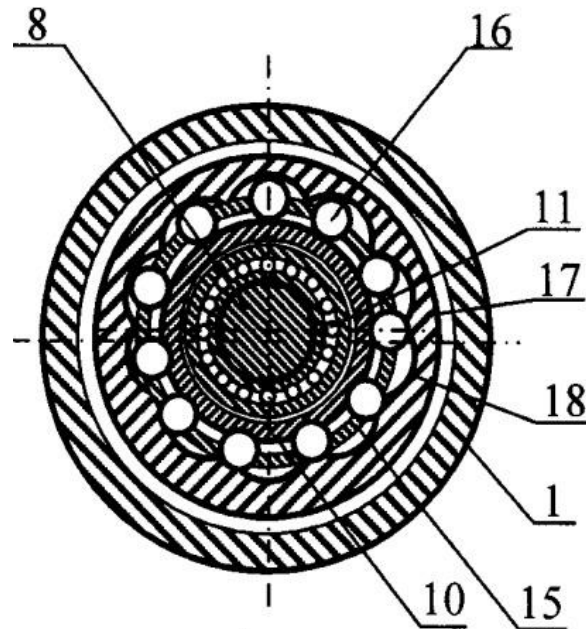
Розріз А-А, хвильова передача в розрізі: 1 – корпус; 8 – вал ротора; 10 – ексцентрики; 11 – підшипники; 15 – сепаратор; 16 – тіла обертання; 17 – жорстке колесо; 18 – хвильова поверхня;
